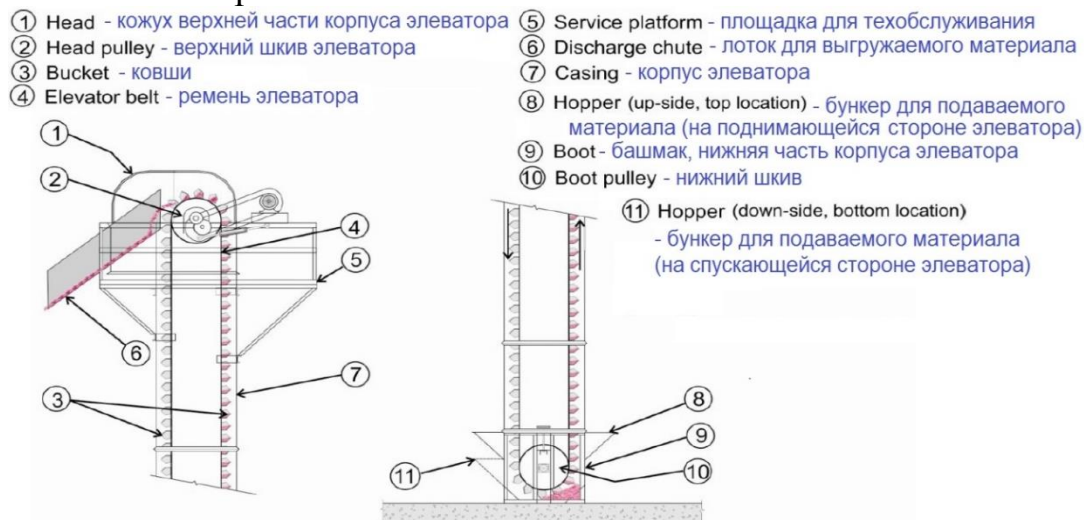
Схемы конструкции и работы ковшового элеватора
